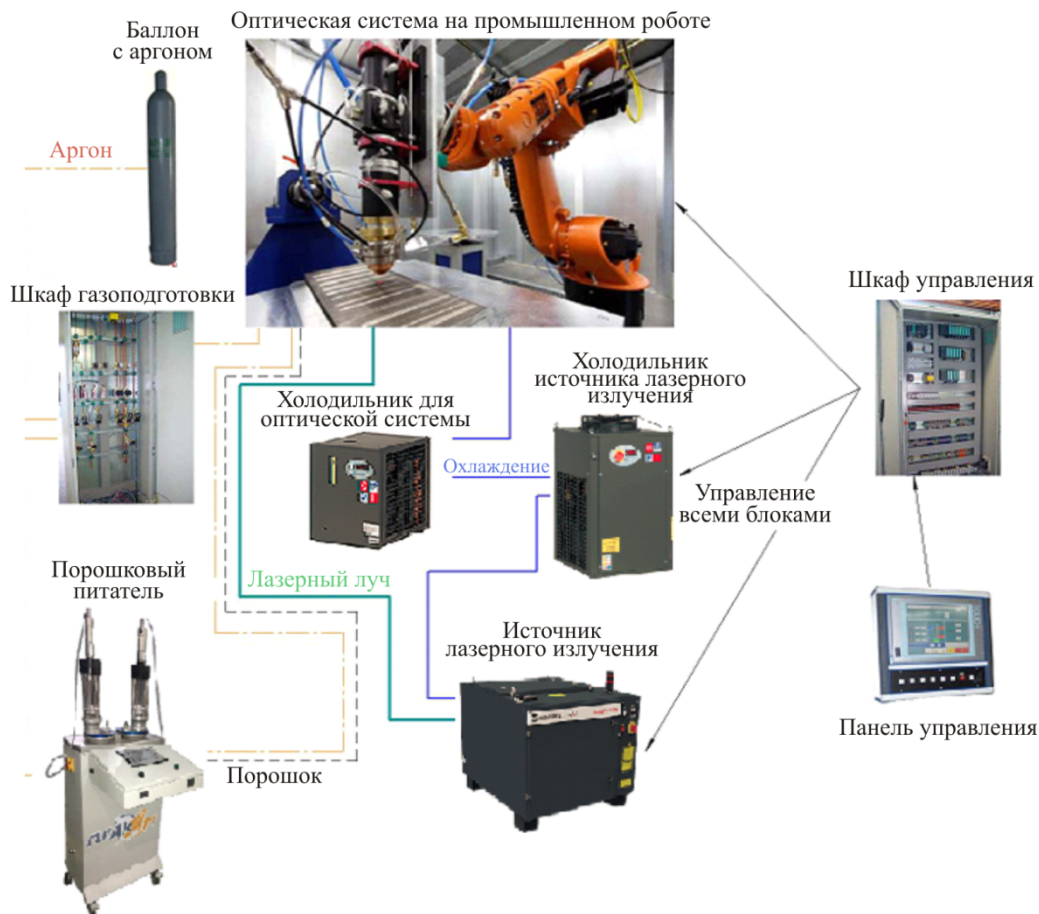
Схема установки лазерной наплавки MLS FL 040
